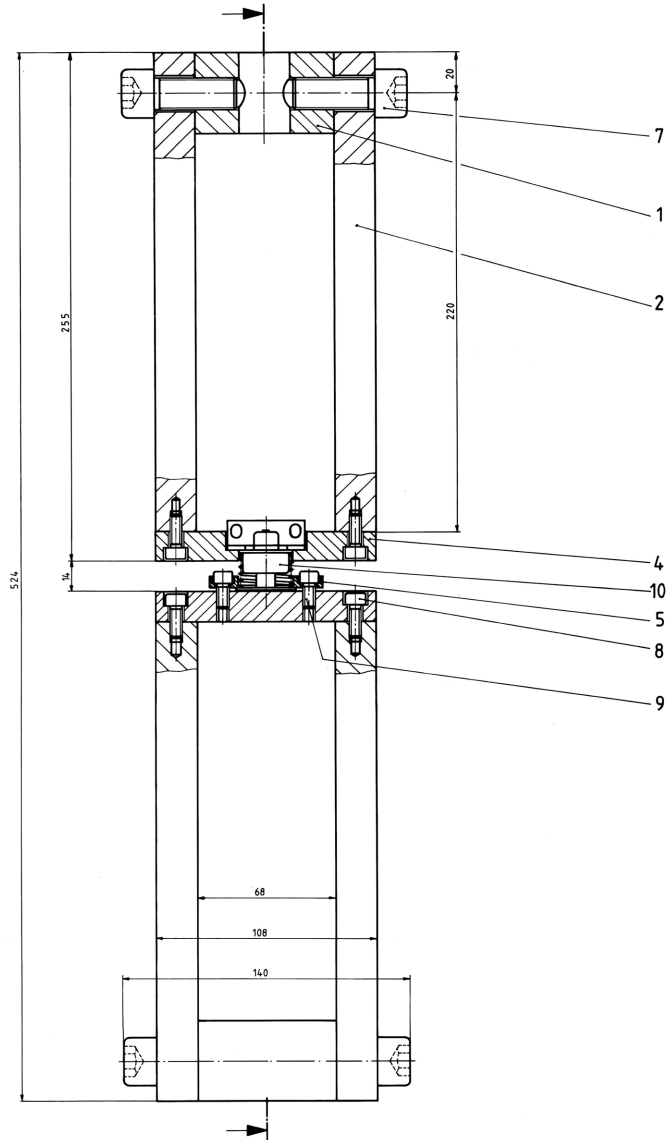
Probenaufnahme für Druck-Druckverschlüsse
